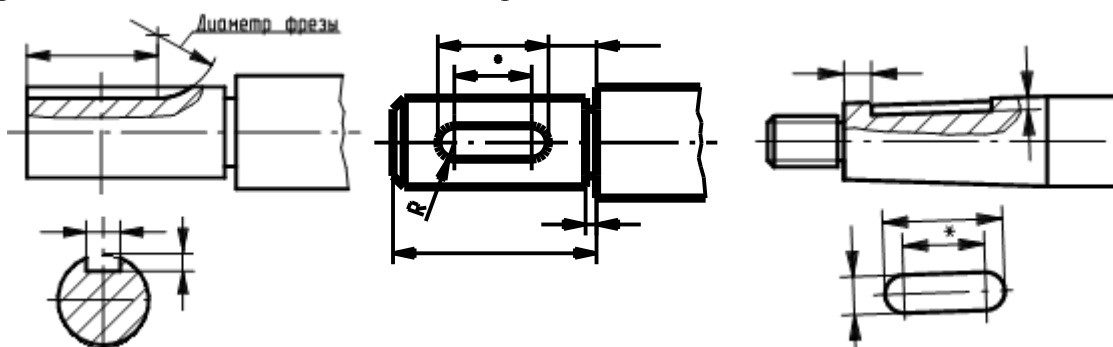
Типовые схемы нанесения размеров шпоночного паза
